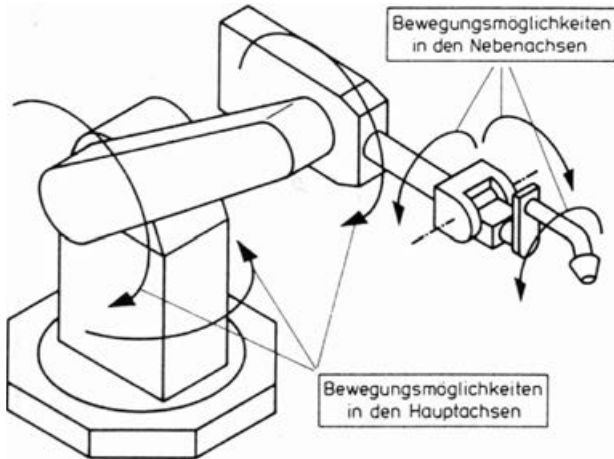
Beispiel für einen sechssachsigen Industrieroboter zum Schutzgasschweißen.
